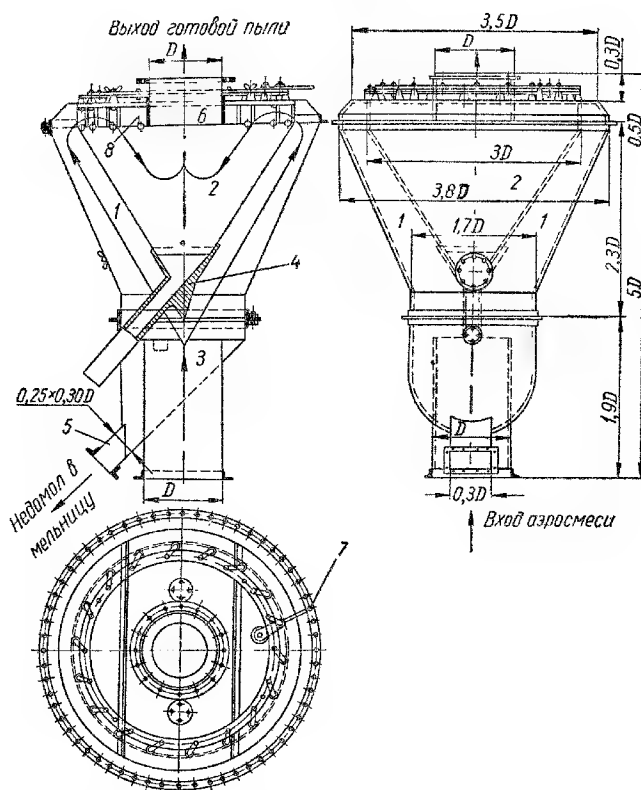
Центробежный сепаратор с поворотными лопатками:
